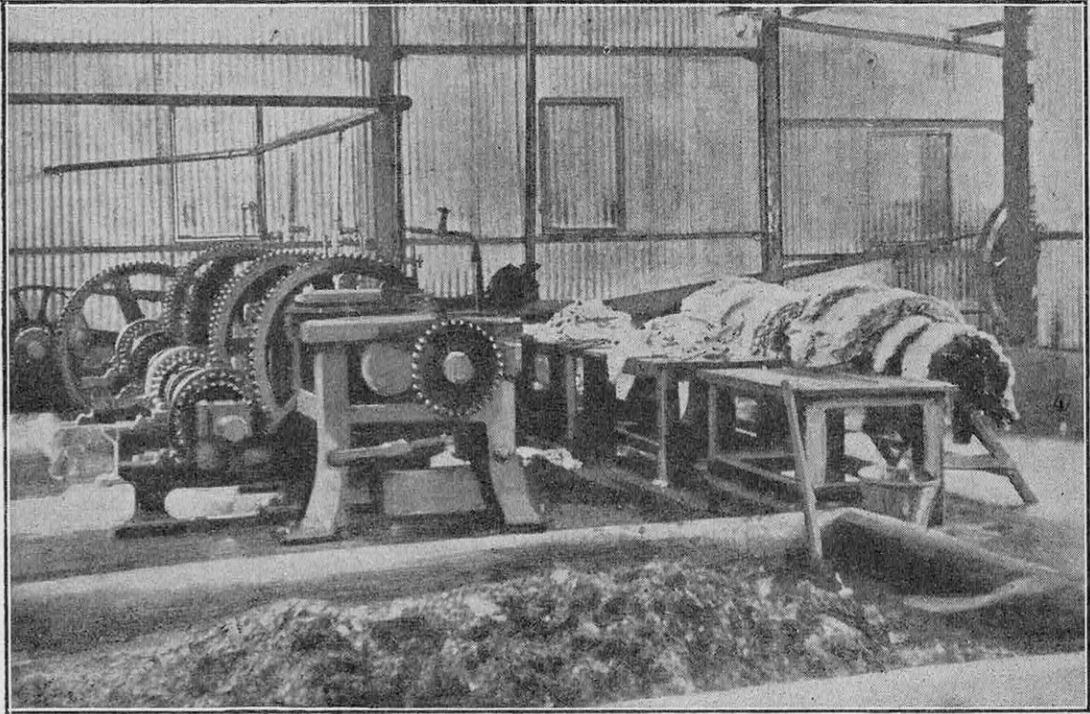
MACHINE MODERNE A FABRIQUER LES CRÊPES DE CAOUTCHOUC, PAR LAMINAGE DU LATEX COAGULÉ
